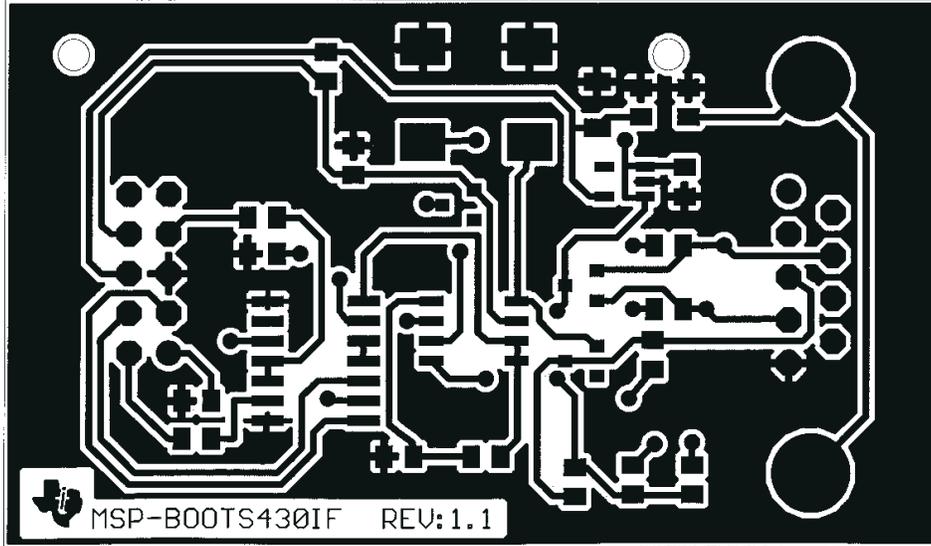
通用 BSL 接口 PCB 布局，顶视图
